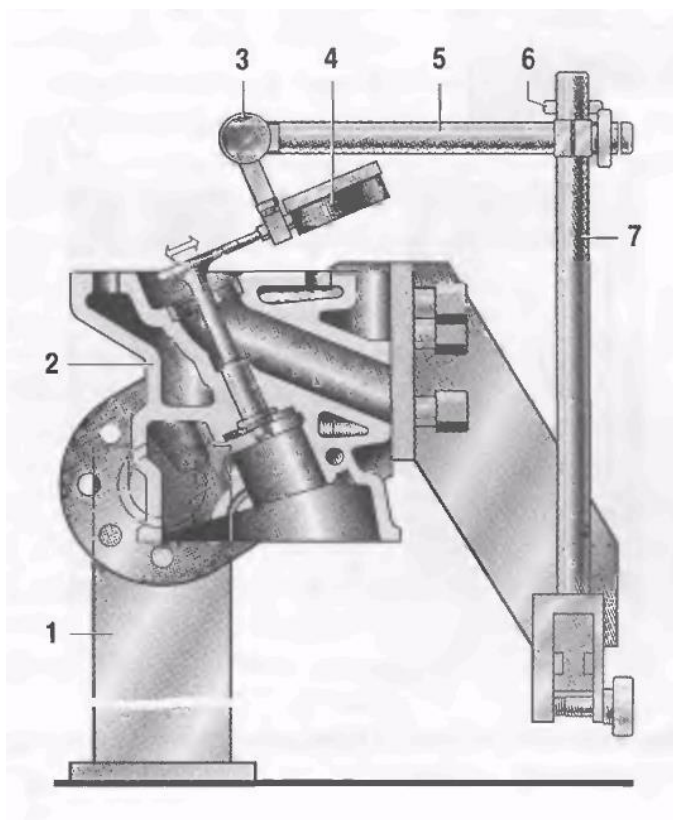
Пристосування до стенду для перевірки зазору між стрижнем клапана і втулкою: 1 – оригінальний стенд для головок блоків циліндрів (рис. 5.2); 2 - головка блоку; 3 - кріплення індикатора; 4 - індикатор; 5 - горизонтальна штанга; 6 - з'єднання штанг; 7 - вертикальна штанга зі скобою.
